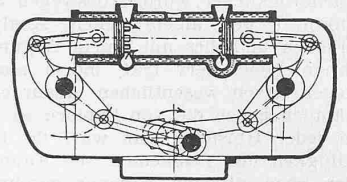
Gegenkolbenmotor mit seitlichen Schwinghebeln
